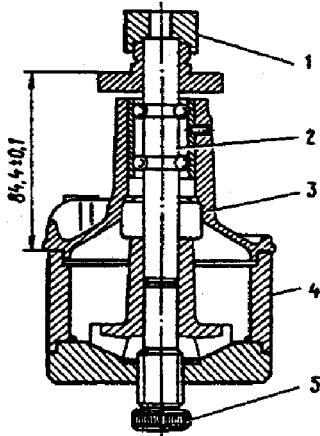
Montagem do cubo da polia: 1 - apoio; 2 - eixo da bomba; 3 - tampa do corpo da bomba; 4 - suporte; 5 - parafuso posicionador.
